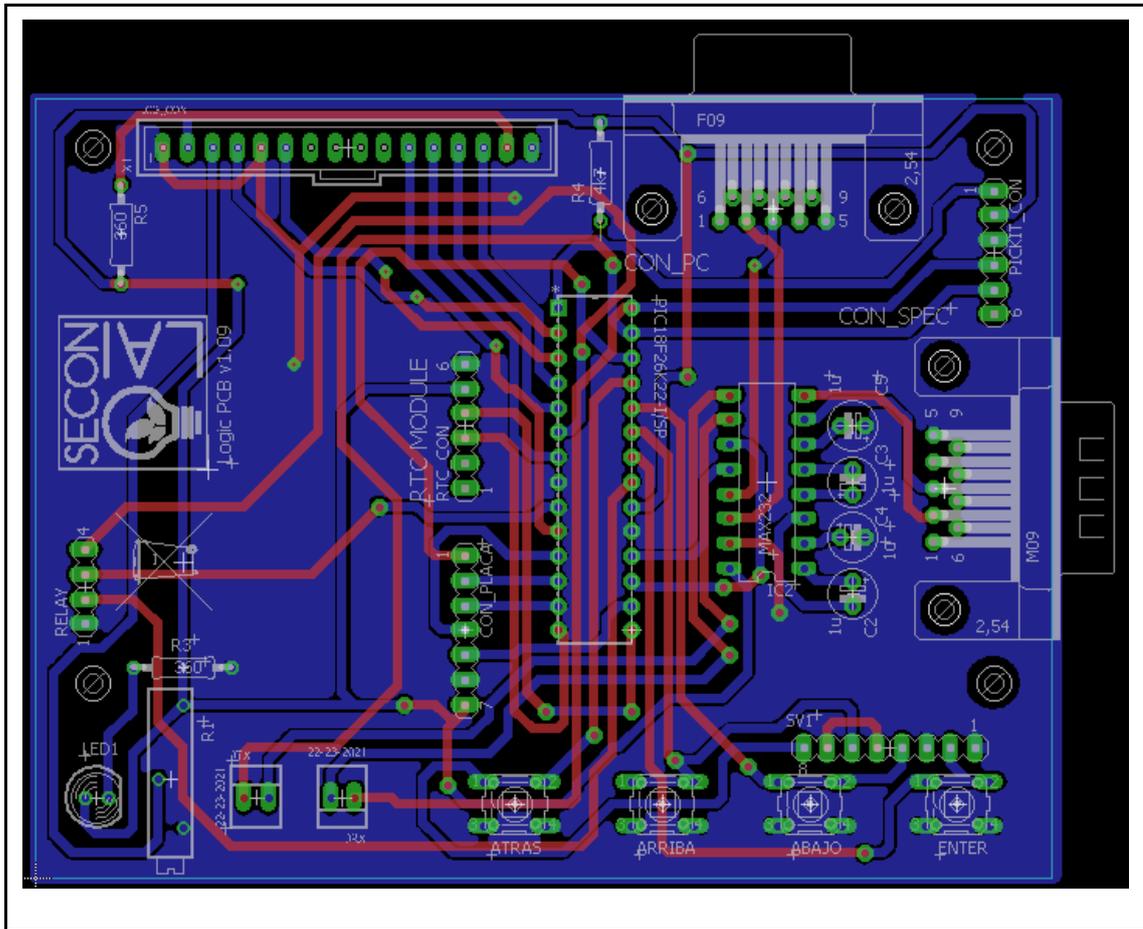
DISEÑO Y RUTEO DE PCB DE LÓGICA.
